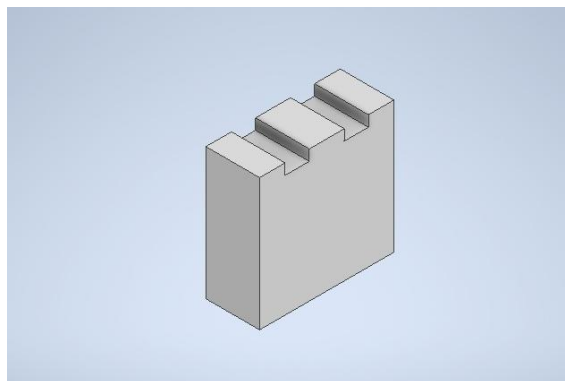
Diseño 3D de la pieza "Apoyo_rampa" en Autodesk.
